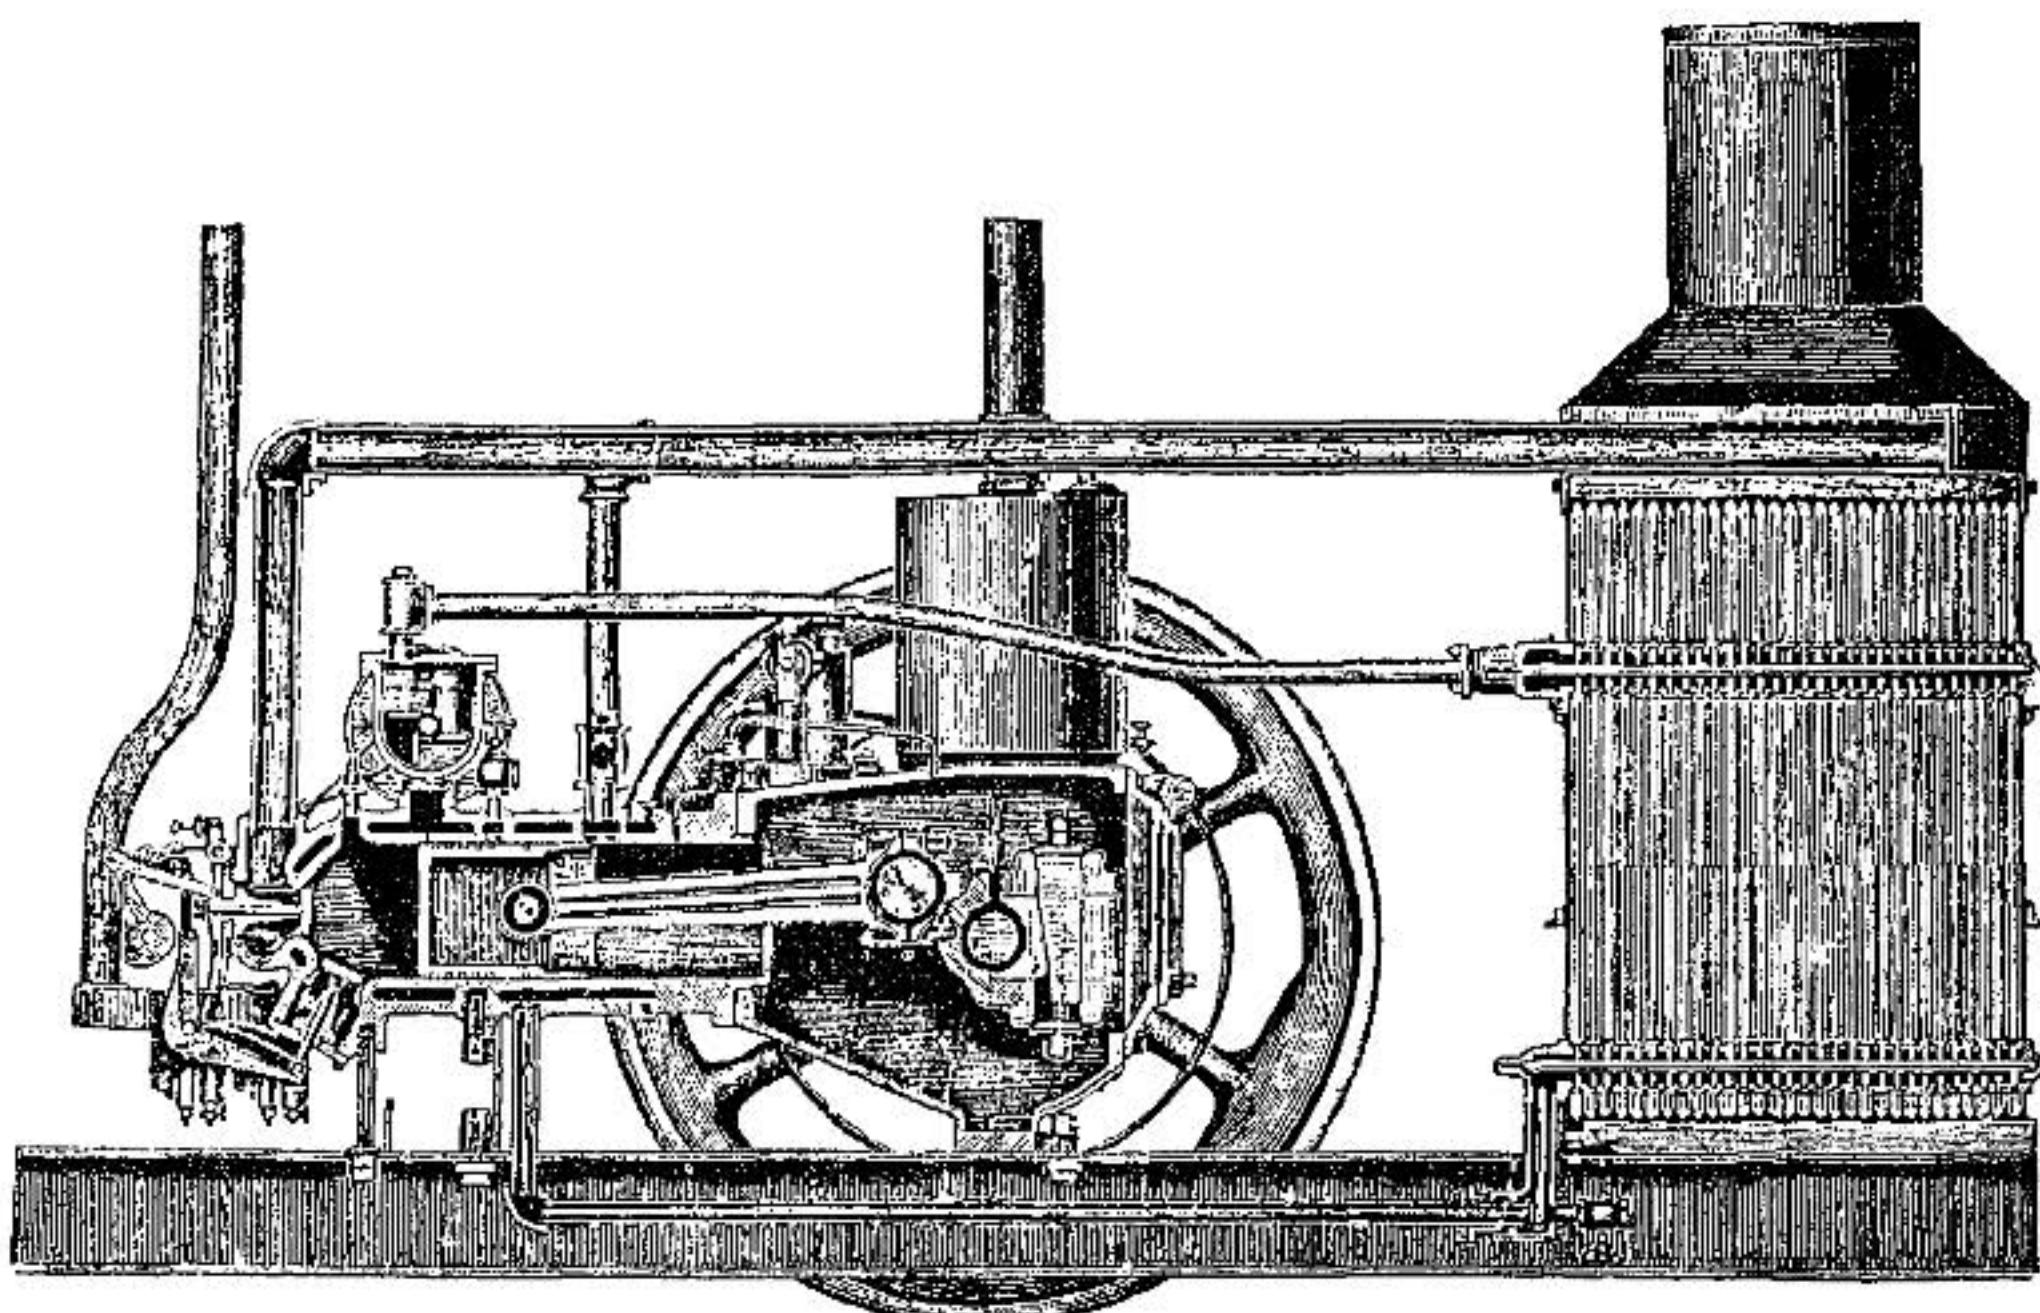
Схематический разрѣзъ двигателя Гартъ-Парръ.
